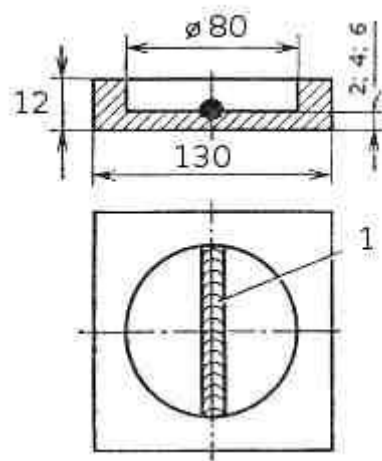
Кондуктор для сборки под сварку составных пластин
